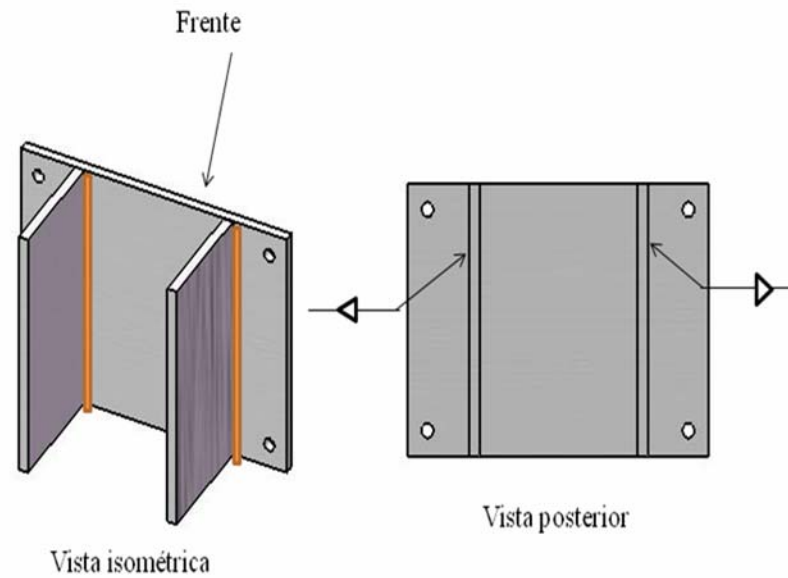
Soldadura entre las tres planchas. [Fuente propia]
